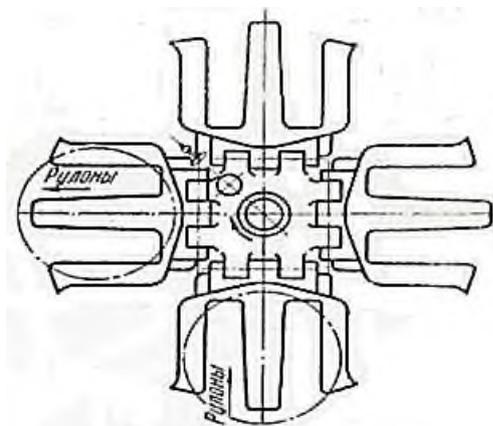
Общий вид подъемно-поворотного стола для рулонов горячекатаной полосы [5]
